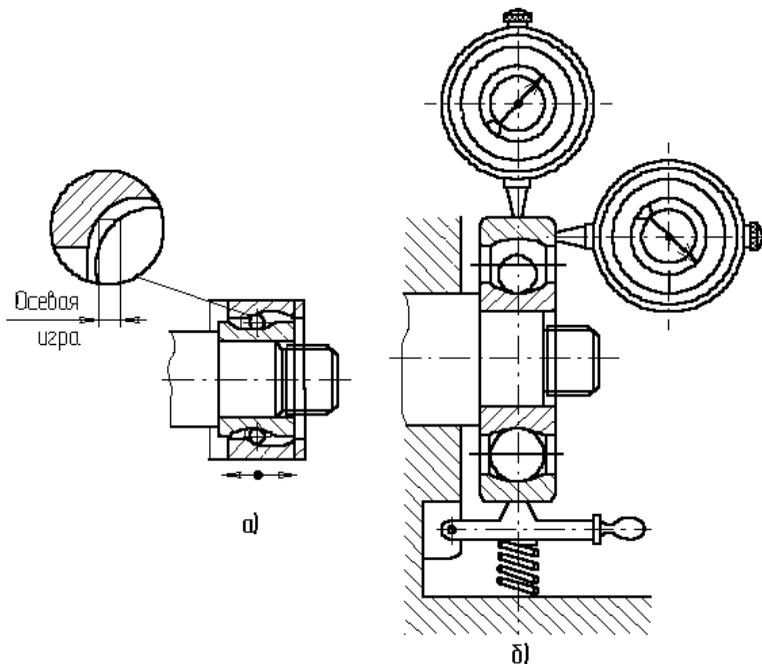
Схема проверки зазоров в подшипнике после его напрессовки на вал: а) «на качку»; б) в приспособлении
